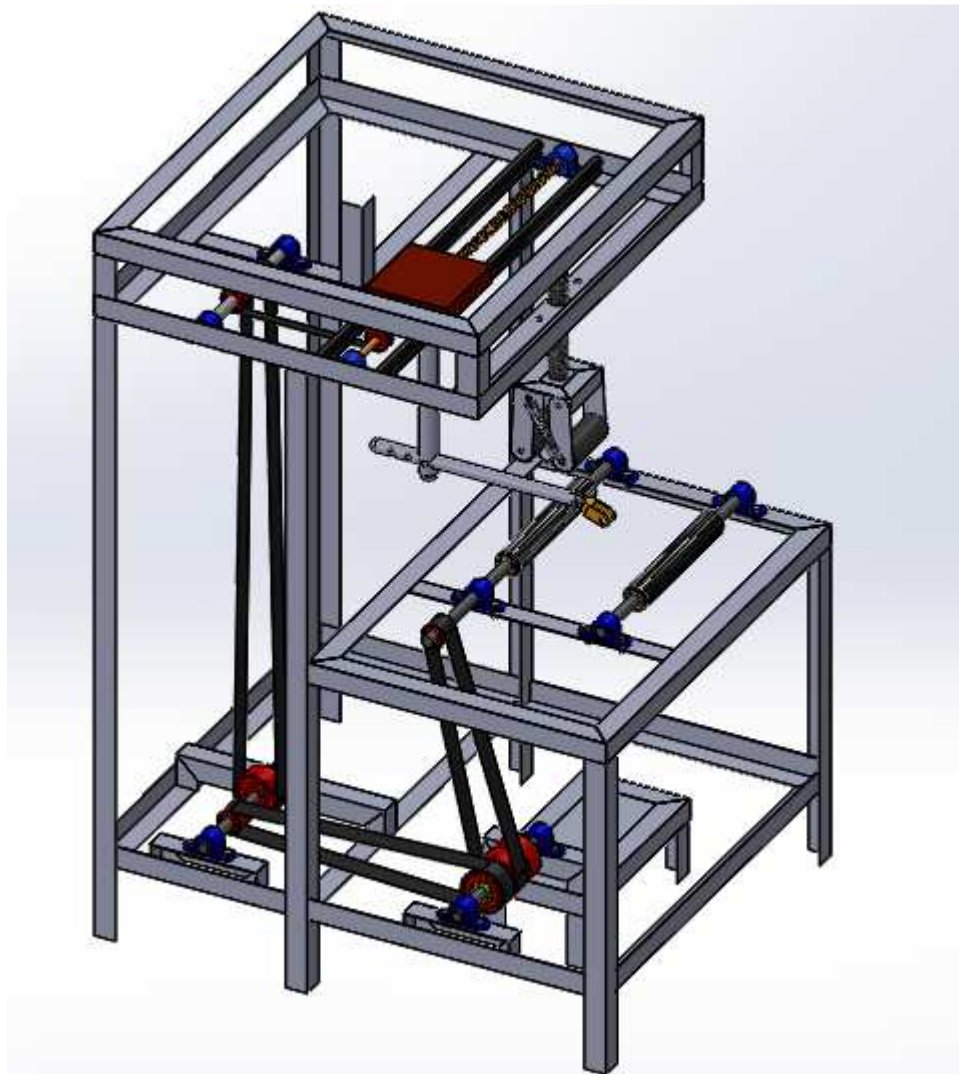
Mecanismo propuesto para la máquina semiautomática para asistir el proceso de soldadura MIG/MAG para recipientes a presión.
